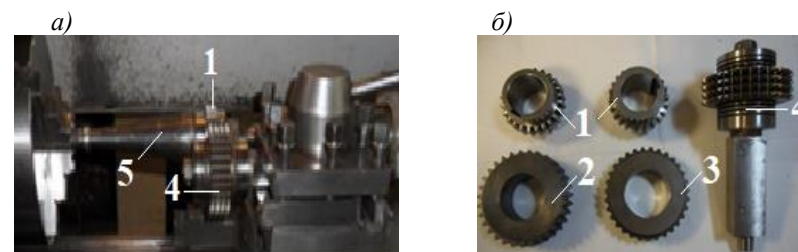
Процесс обработки, конструкция обкатного инструмента и обработанные заготовки: а – процесс обработки; б – конструкция обкатного инструмента и обработанные заготовки; 1 – обработанные зубчатые колеса Ст40Х, $m = 2÷5$, $z = 24$; 2 – шевер-прикатник Р6М5; 3 – шевер-прикатник ШХ15; 4 – инструмент в сборе; 5 – оправка для установки заготовок
